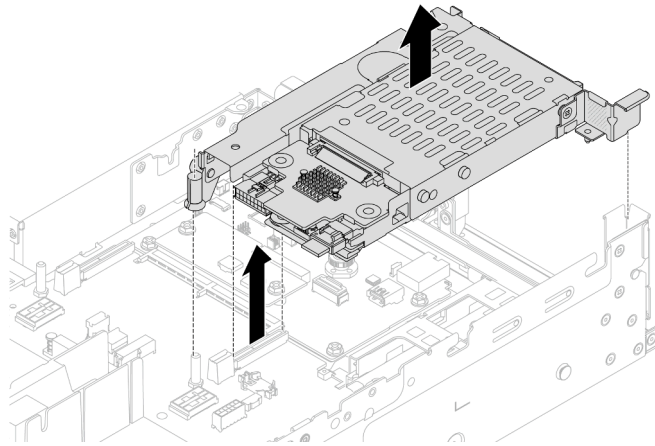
Entfernen des 7-mm-SSD-Adapterrahmens
